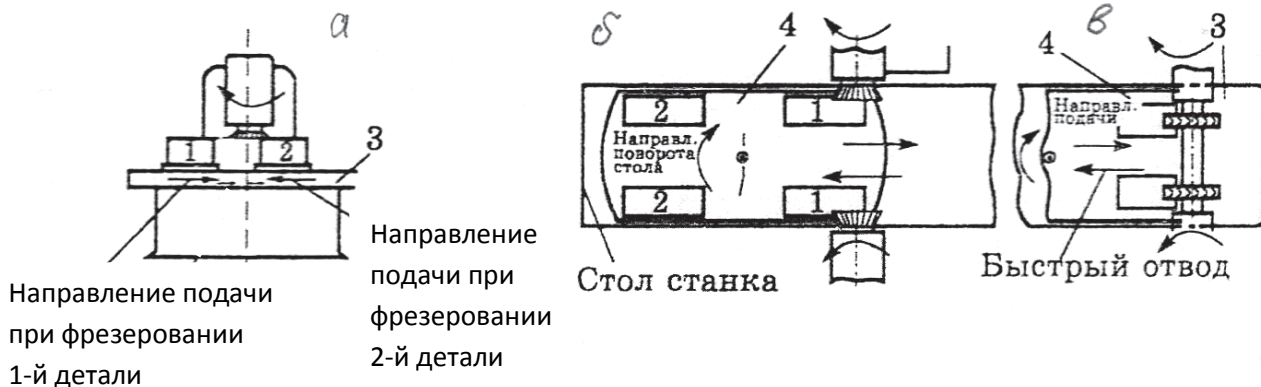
Производительные методы фрезерования: 1, 2 – обрабатываемые детали; 3 – стол станка; 4 – поворотный стол
